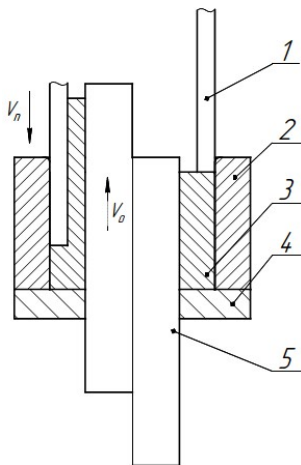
Схема процесу холодного формування фланців в трубчастій заготовці з застосуванням активних сил тертя (1 – пунсон, 2 – контейнер, 3 – заготовка, 4 – нижня плита, 5 – оправка)
